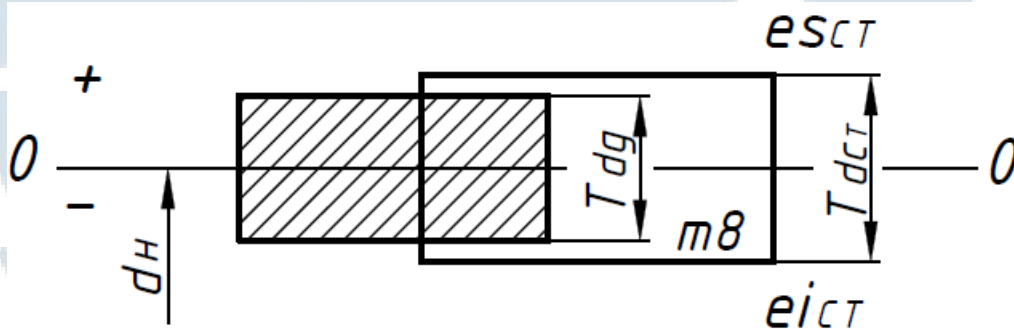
Схема расположения полей допусков (действительного и стандартного) вала
